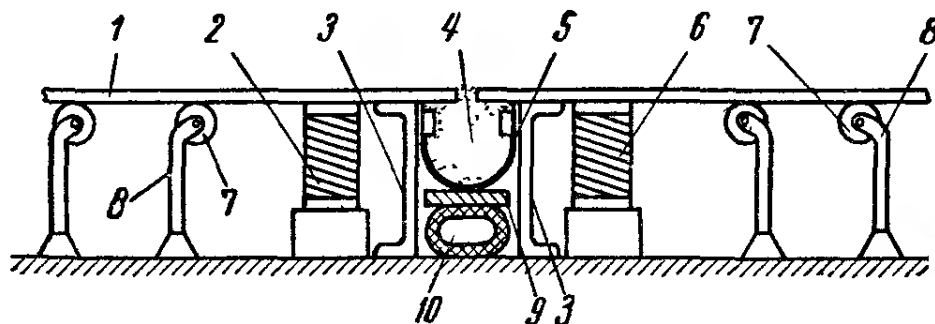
Схема флюсовой подушки с пневматическим прижатием флюса
